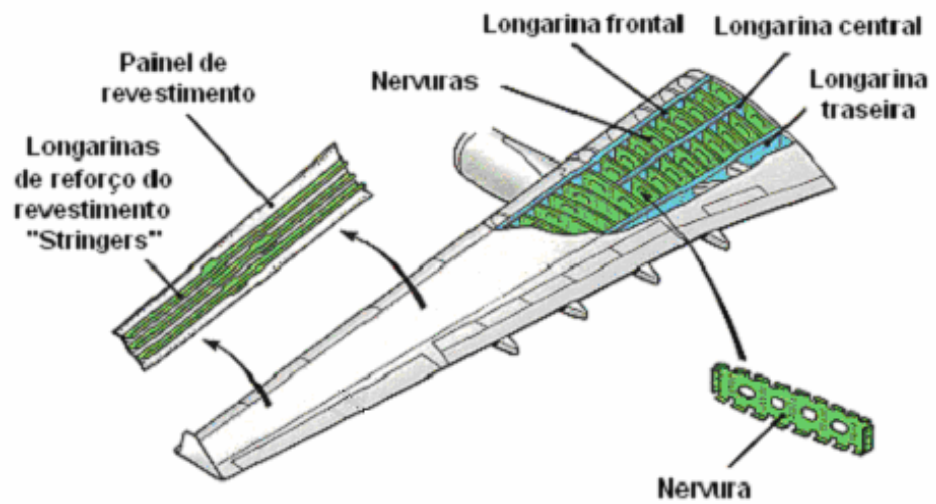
Elementos estruturais utilizados na construção tipo caixa de torção
